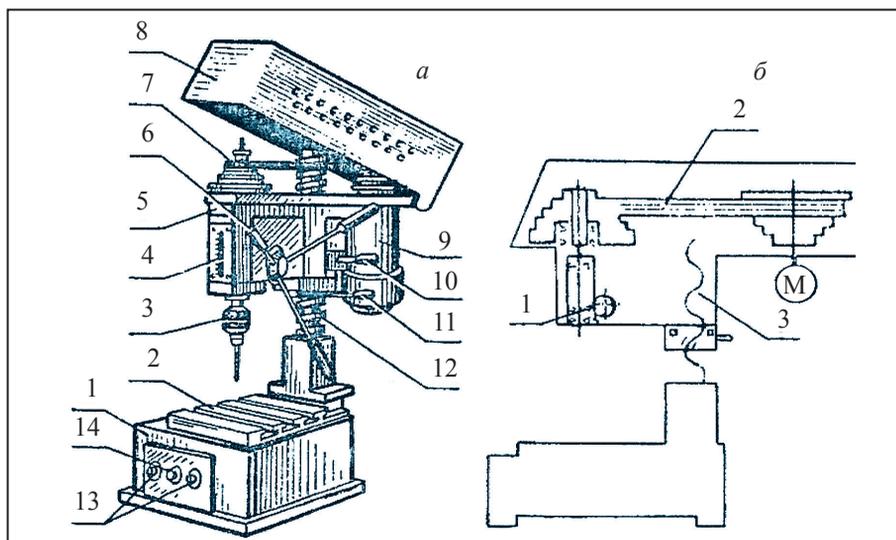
Сверлильный станок: *a* – общее строение (1 – основание; 2 – рабочий стол; 3 – патрон; 4 – шкала установления нарезного углубления; 5 – бабка шпинделя; 6 – приводная ручка; 7 – ленточный привод; 8 – защитный кожух; 9 – электродвигатель; 10 – ручка установки бабки шпинделя; 11 – ручка поднятия и опускания бабки шпинделя; 12 – колонна; 13 – кнопка пуска электродвигателя; 14 – кнопка остановки); *б* – кинематическая схема (1 – реечный привод; 2 – ленточный привод; 3 – винтовой привод).
